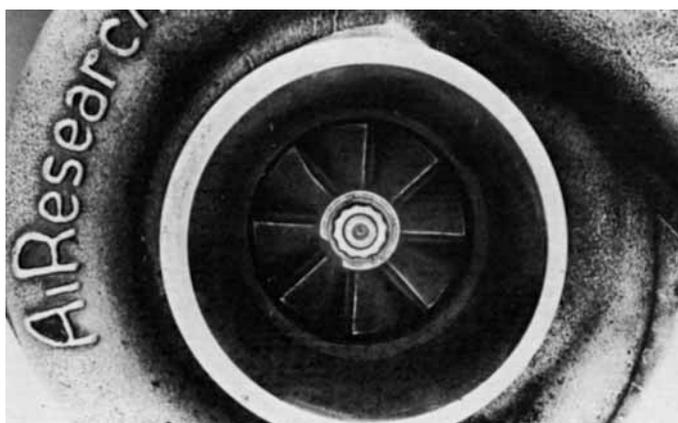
roçamento do rotor do compressor na carcaça do compressor
